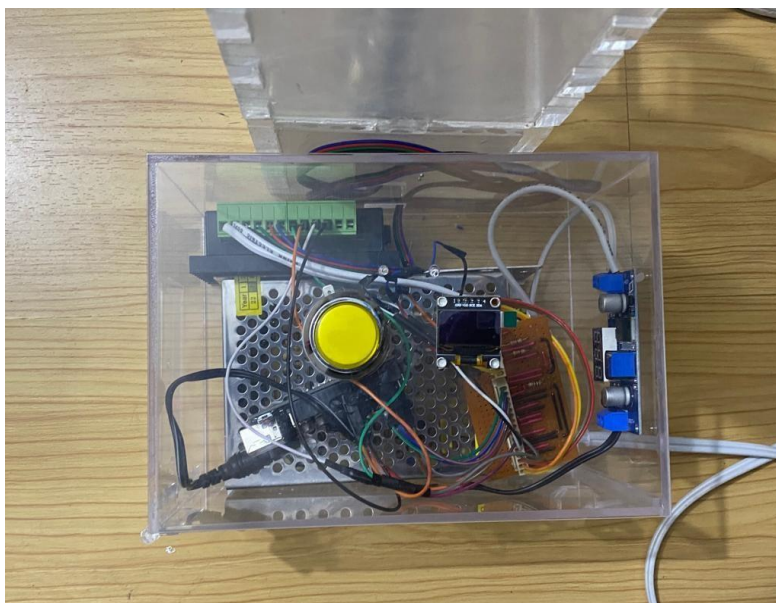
Circuito soldado y ensamblado a los demás componentes electrónicos en la caja de control.
